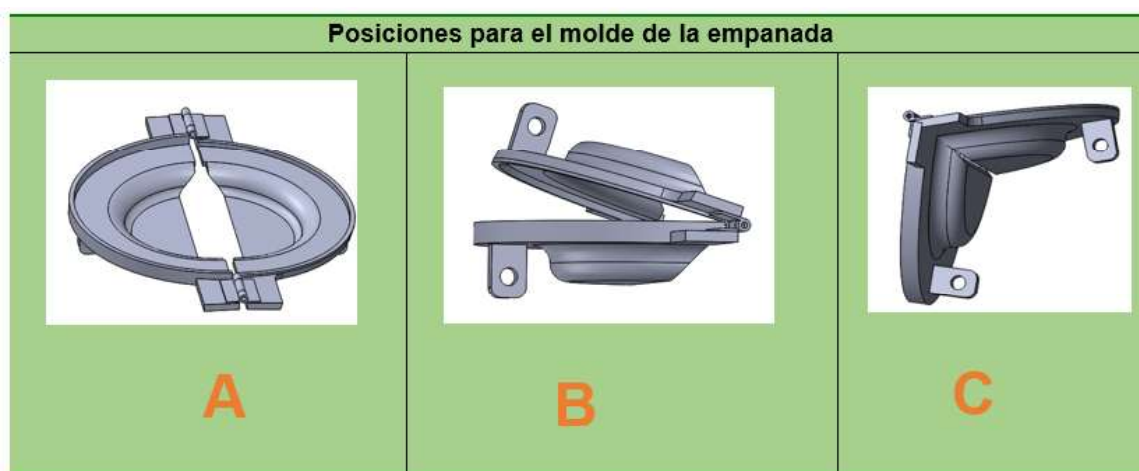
Ensamble de las partes del mecanismo de corte y sellado.
